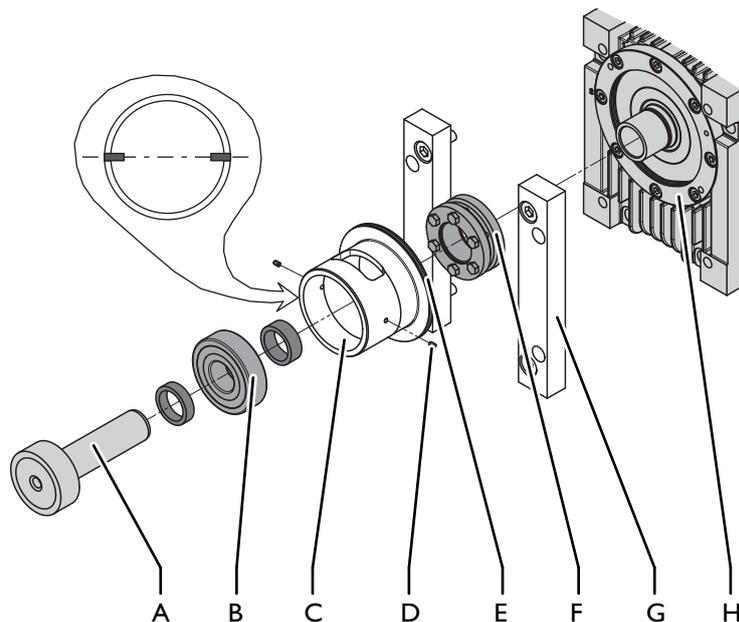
更换小齿轮、轴承和张紧组： Güdel传动装置单元
